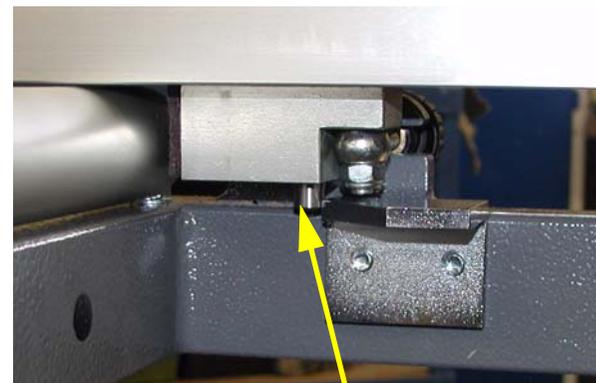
Монтаж углового упора для косых резов WGA_LD
